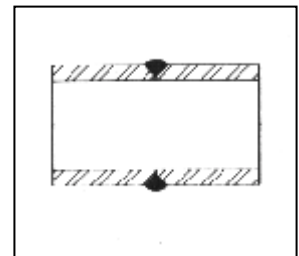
soldadura de caño con penetración incompleta - corrosión severa
